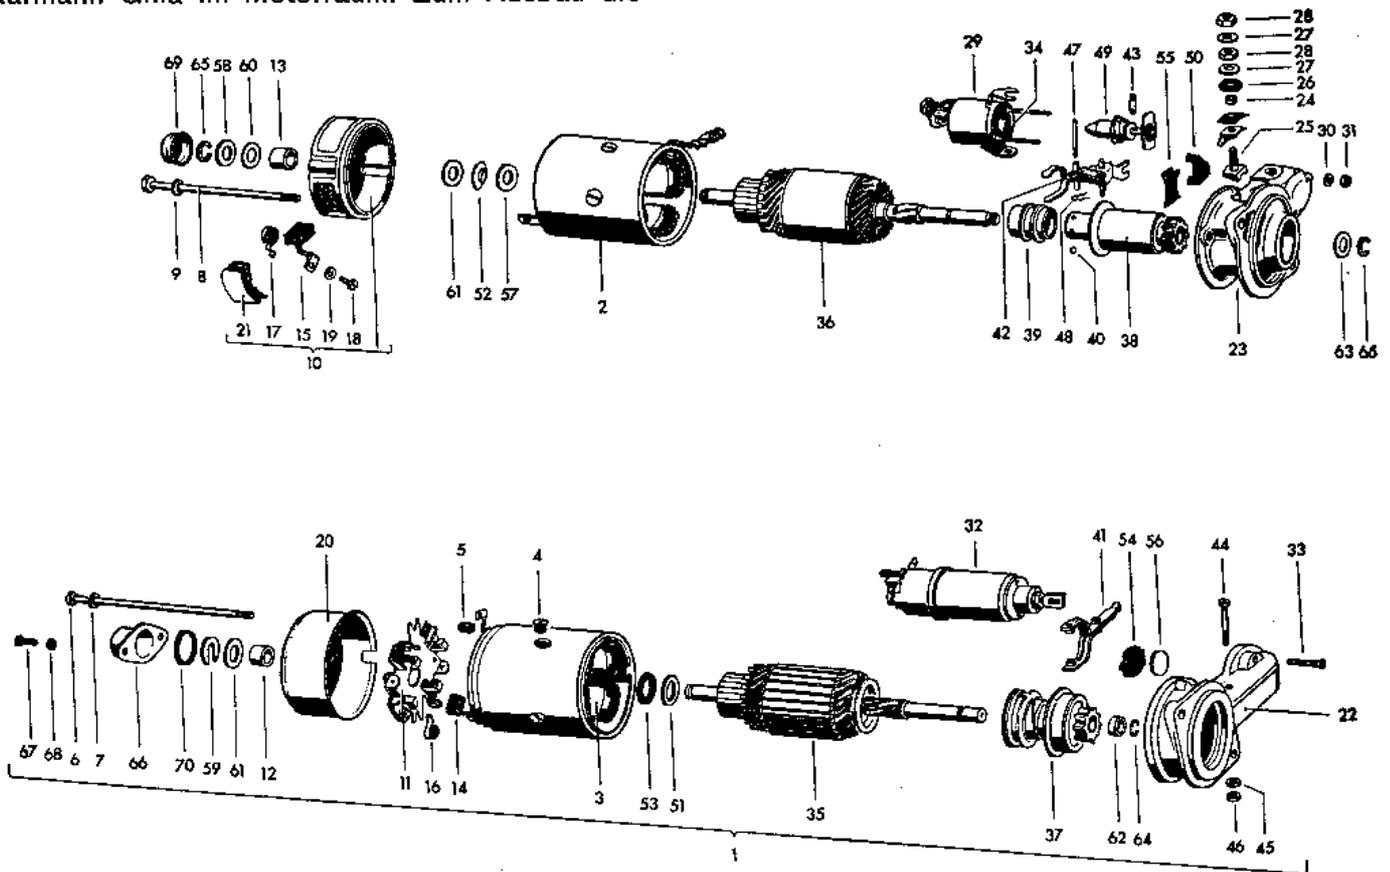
Montagebild eines zerlegten Anlassers. Zwei verschiedene Ausführungen für Fahrzeuge mit Wechselgetriebe sind gezeigt.
